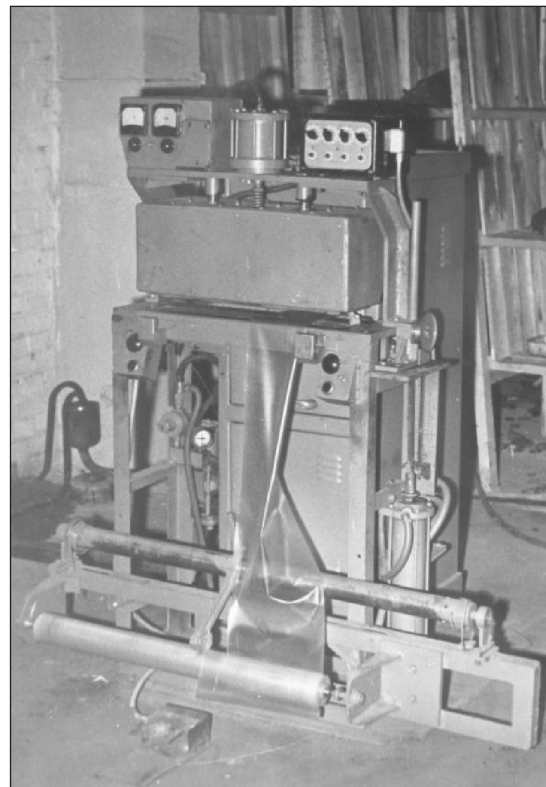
Общий вид установки для сварки полихлорвиниловой пленки
